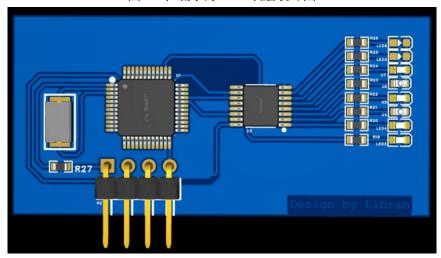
8 位流水灯 PCB 顶层 3D 外壳预览图
